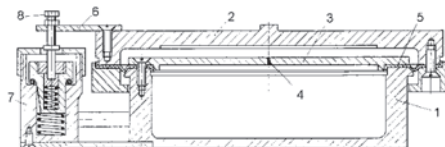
Конструктивная схема пневматической виброизолирующей системы:
